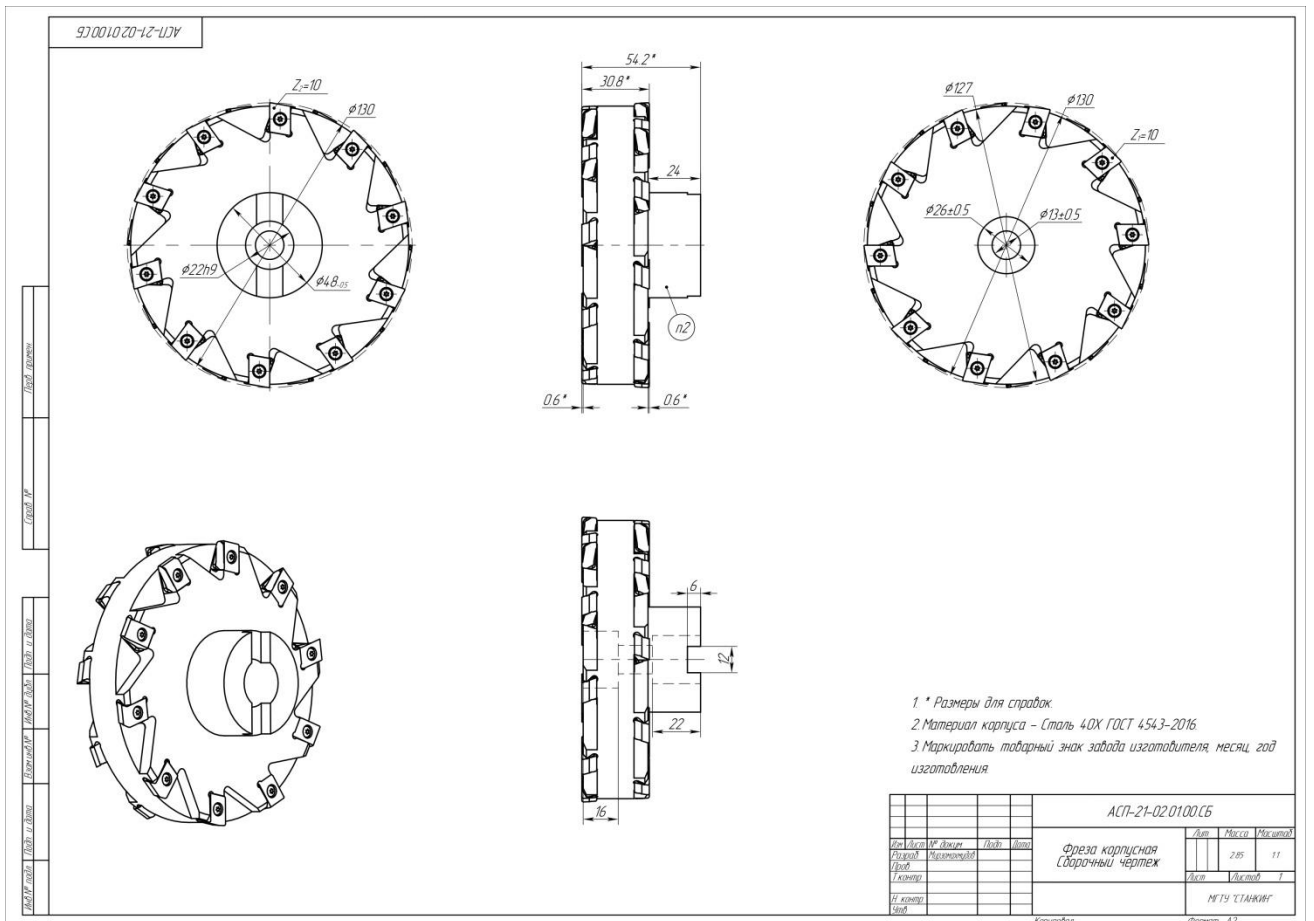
Сборочный чертеж модифицированной по результатам испытаний конструкции сборной дисковой фрезы с СМП.
